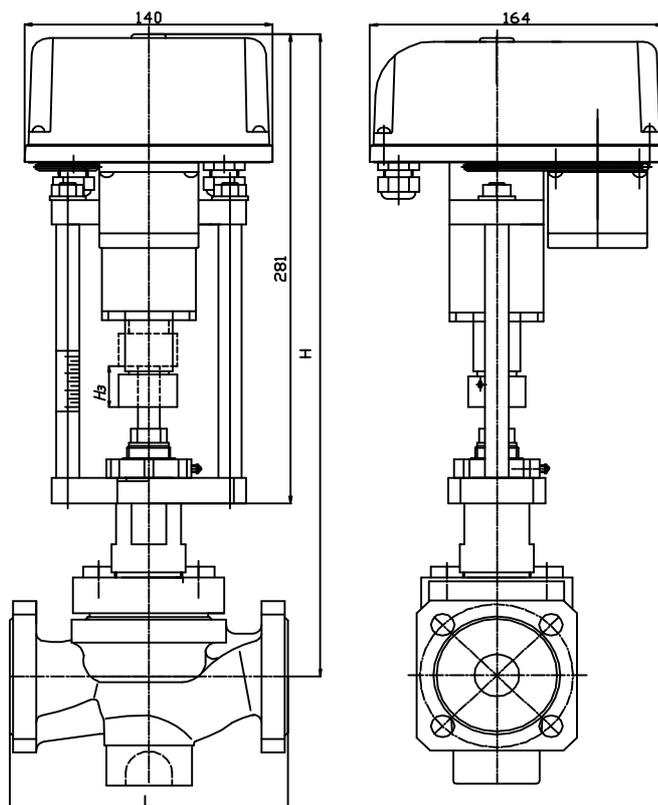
Габаритные установочные и присоединительные размеры клапана.
